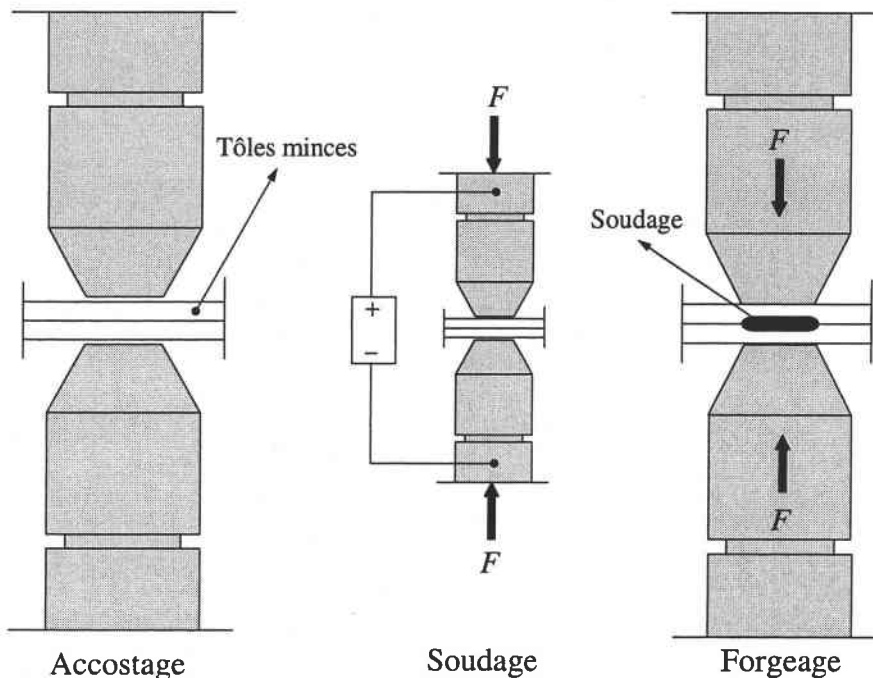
Schéma de la procédure du soudage par point.
